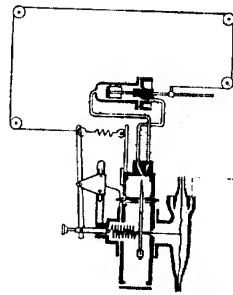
Mechanische Rückführung an einem Regler mit Drucköltrieb.
